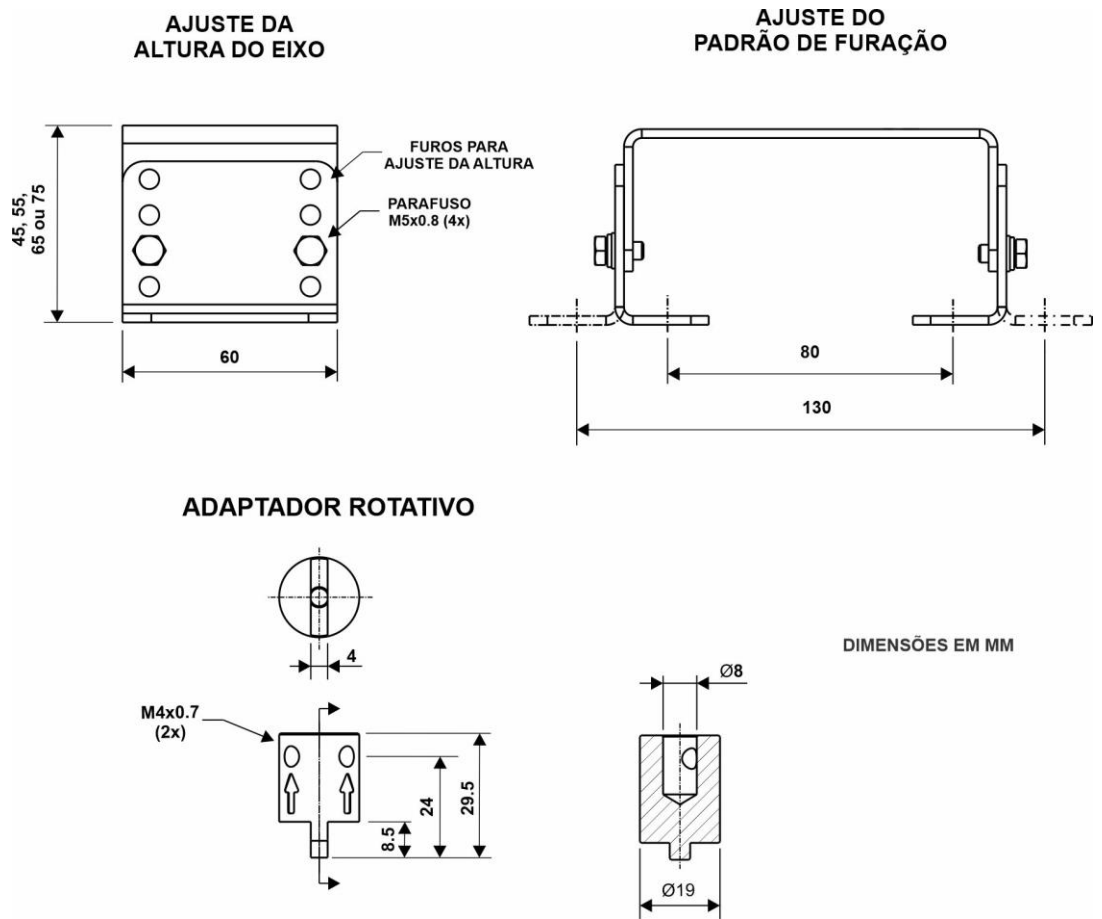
Configuração do suporte de montagem para atuador rotativo
